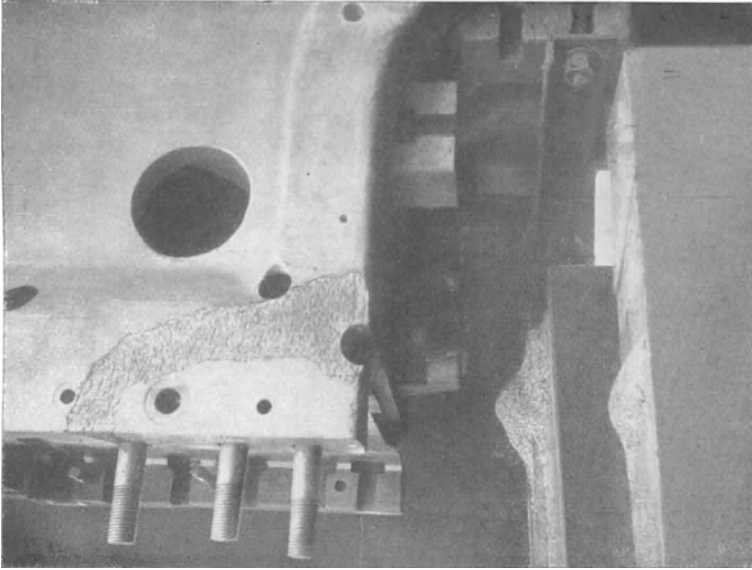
Exzenterpresse, fertig geschweißt.
